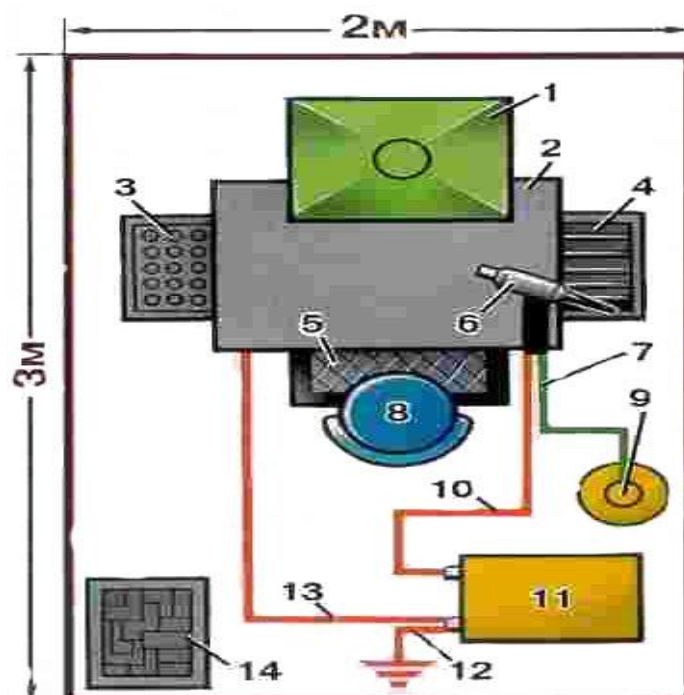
План схема рабочего места сварщика: 1 – вентиляция; 2 – рабочий стол; 3 – ящик для электродов; 4 – ящик для деталей; 5 – диэлектрический коврик; 6 – горелка; 7 – газовый рукав; 8 – стул; 9 – газовый баллон; 10 – прямой провод; 11 – источник питания дуги; 12 – заземление; 13 – обратный провод; 14 – ящик для отходов
